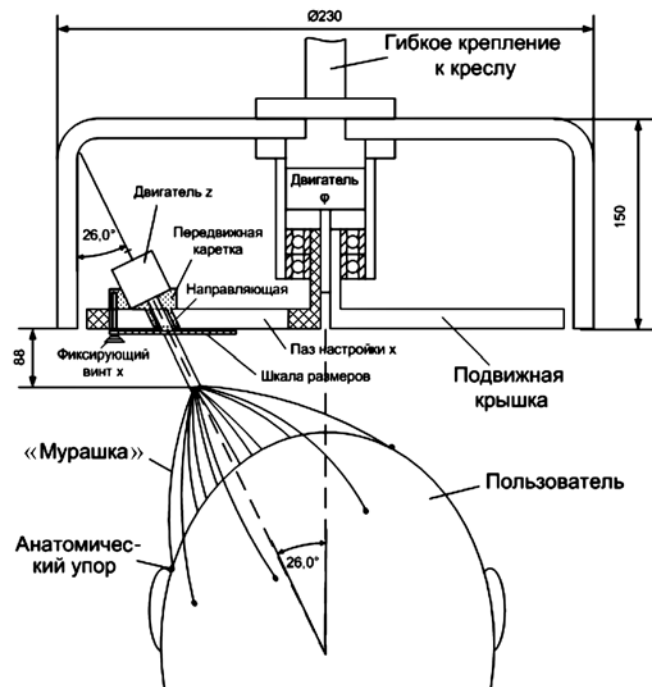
Двухприводной робот с поворотным и линейным электродвигателями
